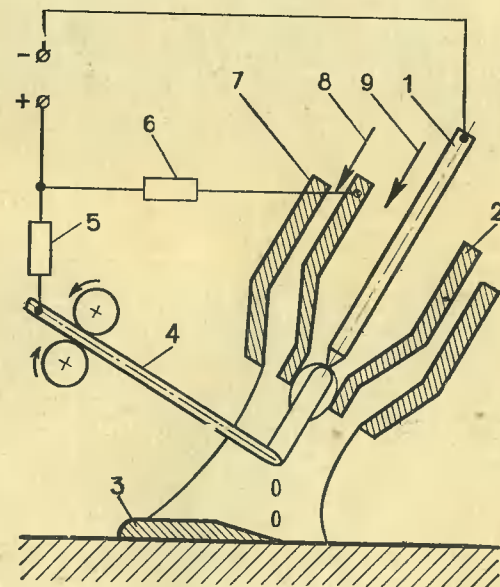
Схема плазменной наплавки с токоведущей присадочной проволокой:
